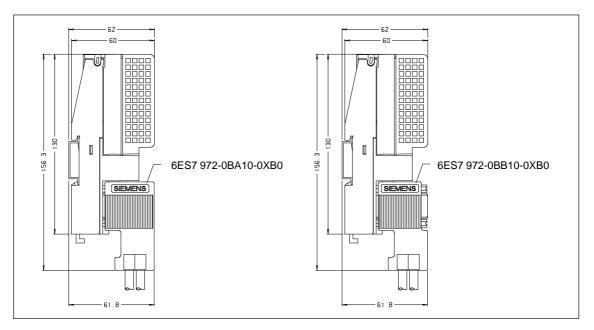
Maßbild: Seitenansicht mit Busanschlußstecker (6ES7 972-0BA10-0XA0 und 6ES7 972-0BB10-0XA0)
